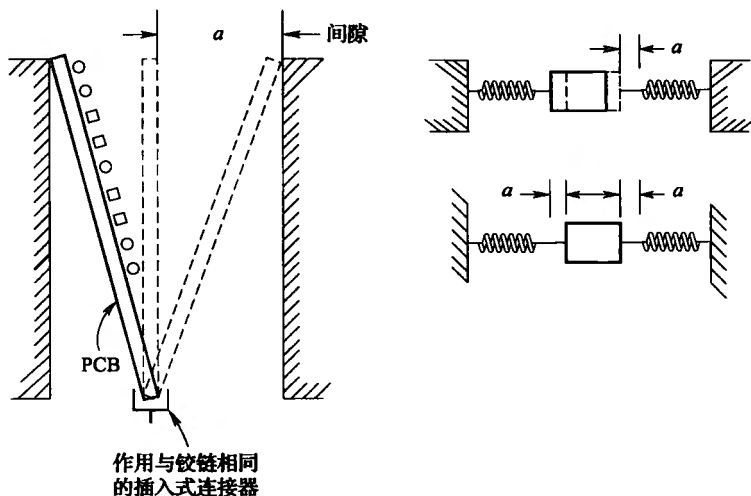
因间隙而松动的边缘导向件使 PCB 前后晃动导致 PCB 谐振频率下降
